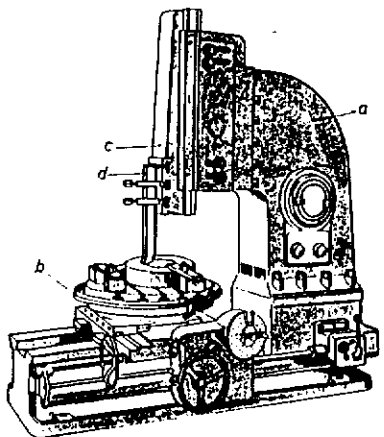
Máquina de mortajar. a) Bastidor; b) mesa o plato; c) carro que lleva el útil; d) portaherramientas.
